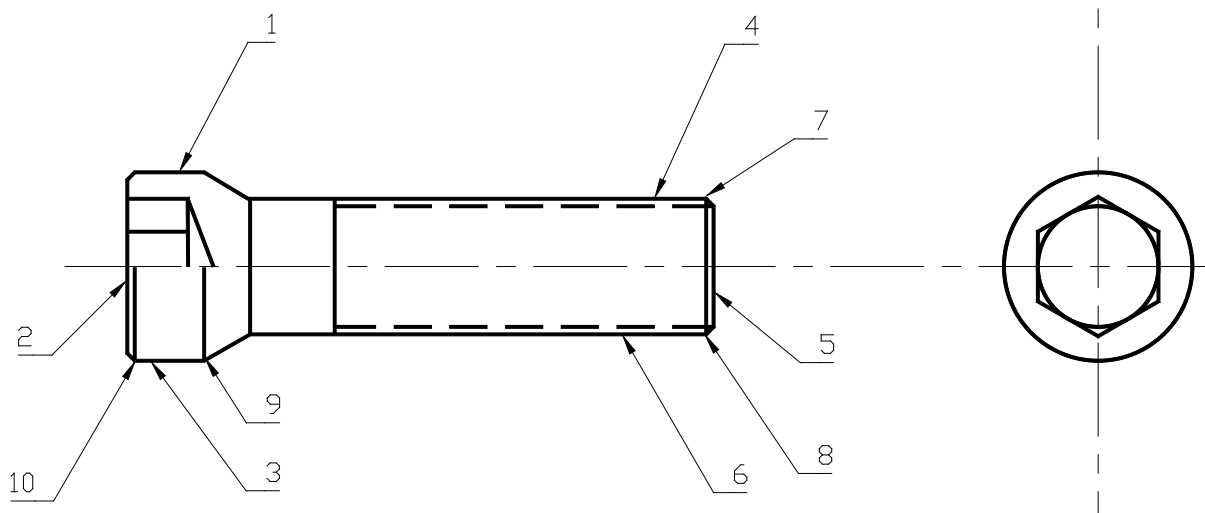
Креслення гвинта після зняття фаски командою CHAMFER
